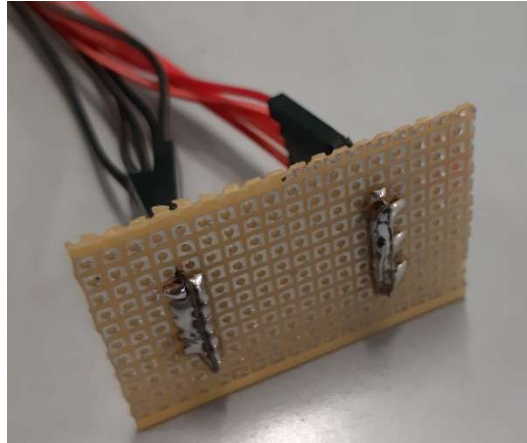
Soldadura de 5 cables amb 5 V i 0 V en una placa de connexions.
